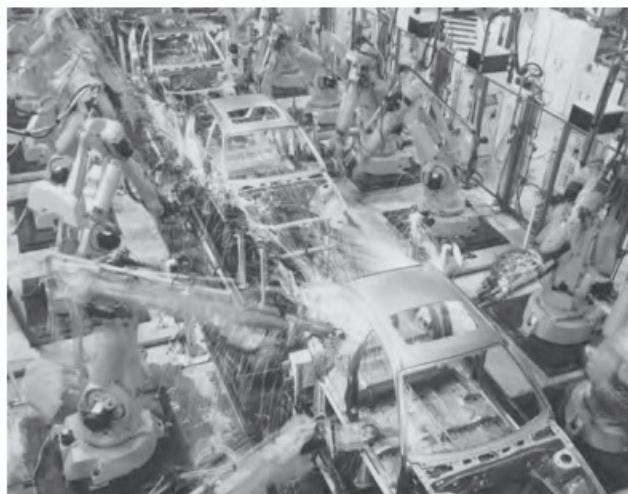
Línea de soldadura por puntos robotizado.
